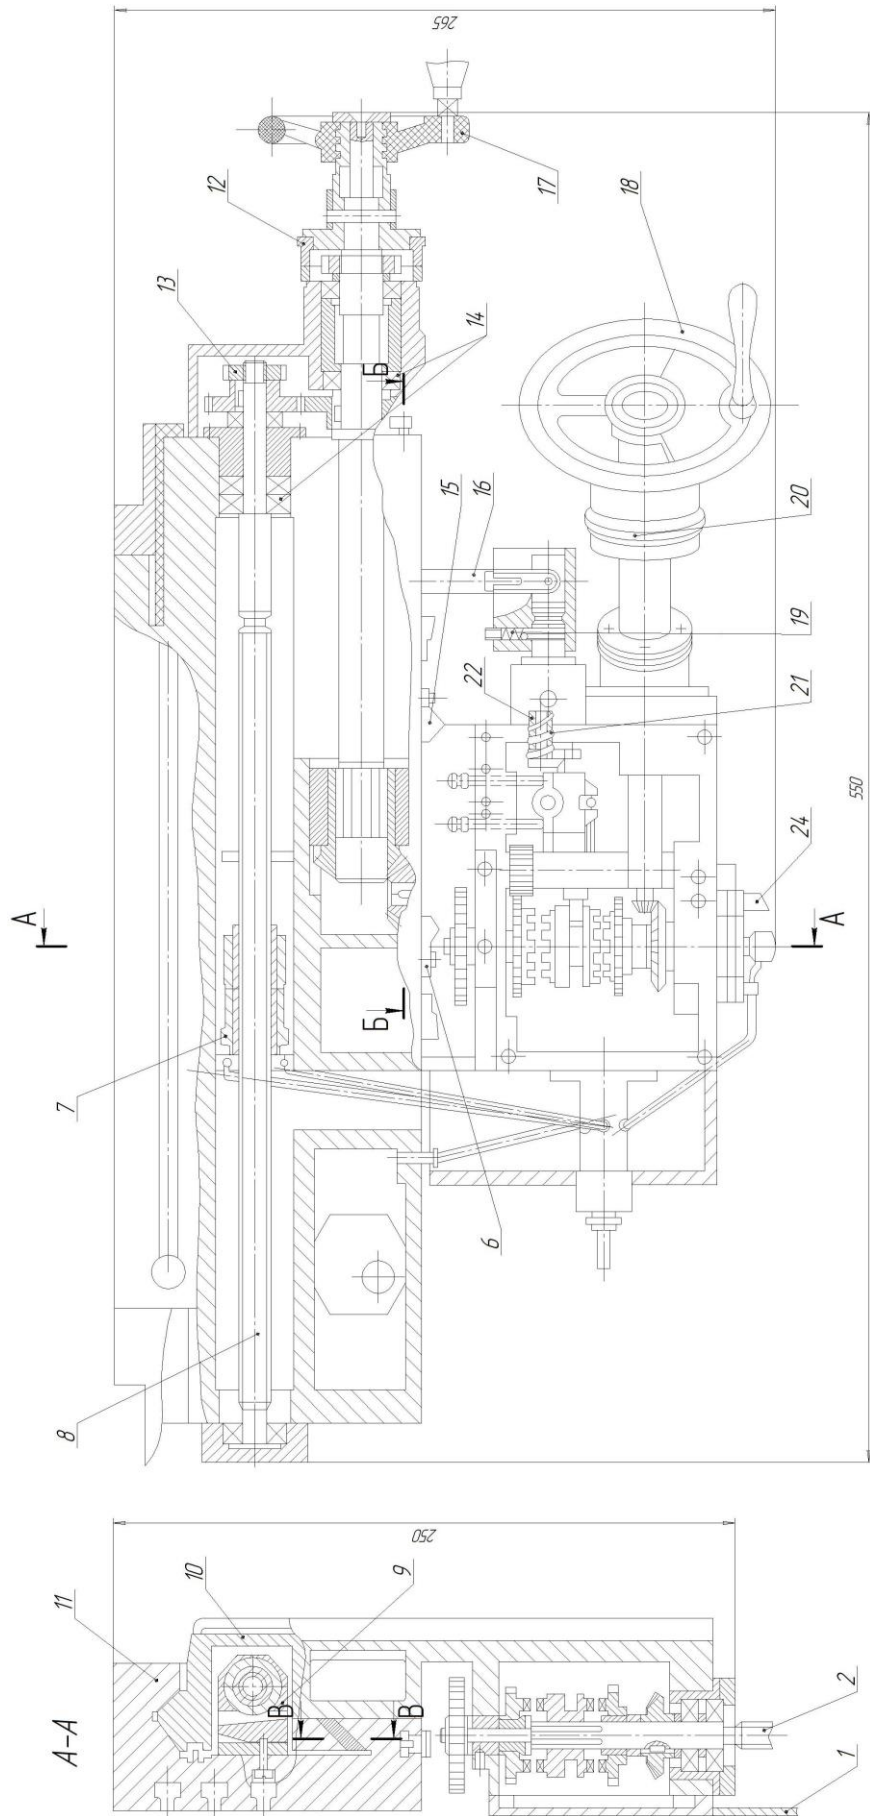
Стіл (супорт) фрезерного верстата
